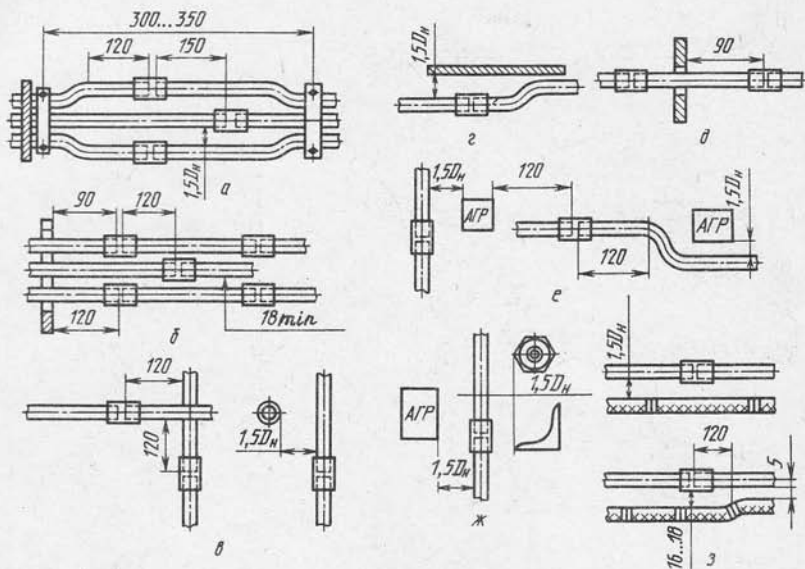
13 Оптимальные зазоры при монтаже систем с неразъемными (паяными и ТМС) соединениями между элементами крепления (а); параллельными трубопроводами (б); перекрещивающимися трубопроводами (в); трубопроводом и гладкой стенкой конструкции (г); трубопроводом и стенкой конструкции (д); трубопроводом и жестко закрепленным агрегатом (е), трубопроводом и острыми кромками деталей (ж); трубопроводом и электрожгутом (з)
